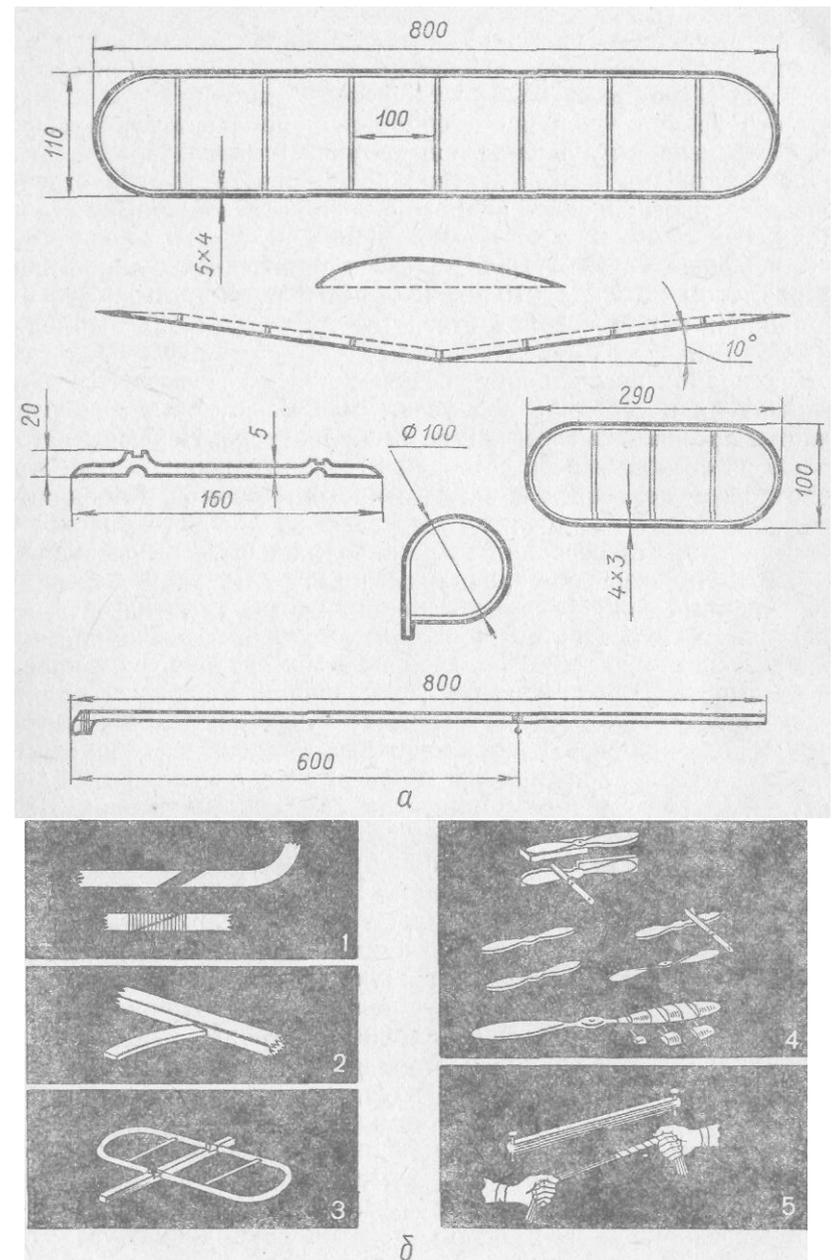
Рабочий чертеж (а) и порядок изготовления схематической модели самолета (б):
